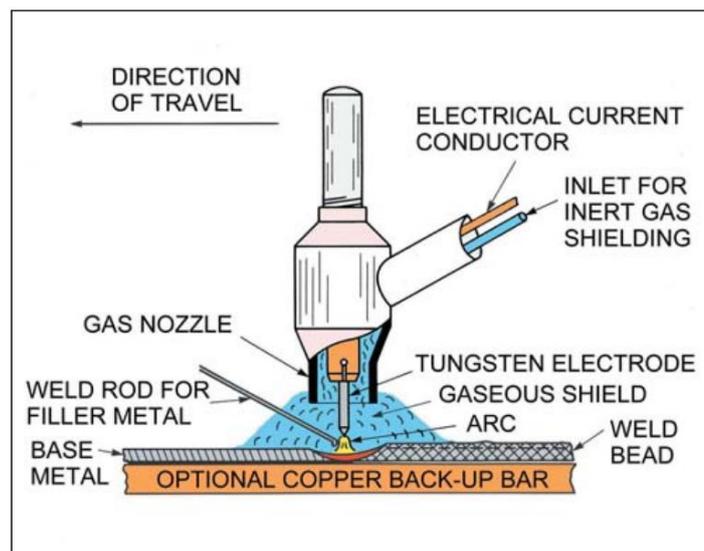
Representação esquemática da soldadura GTAW (AWS, 2001).
